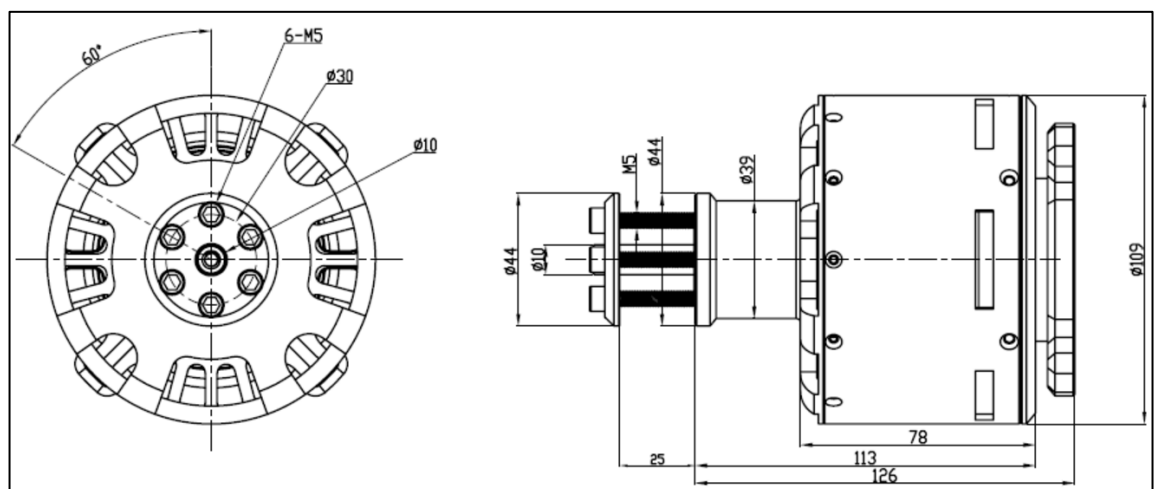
Dimensiones del motor Turginy Rotomax 150cc
